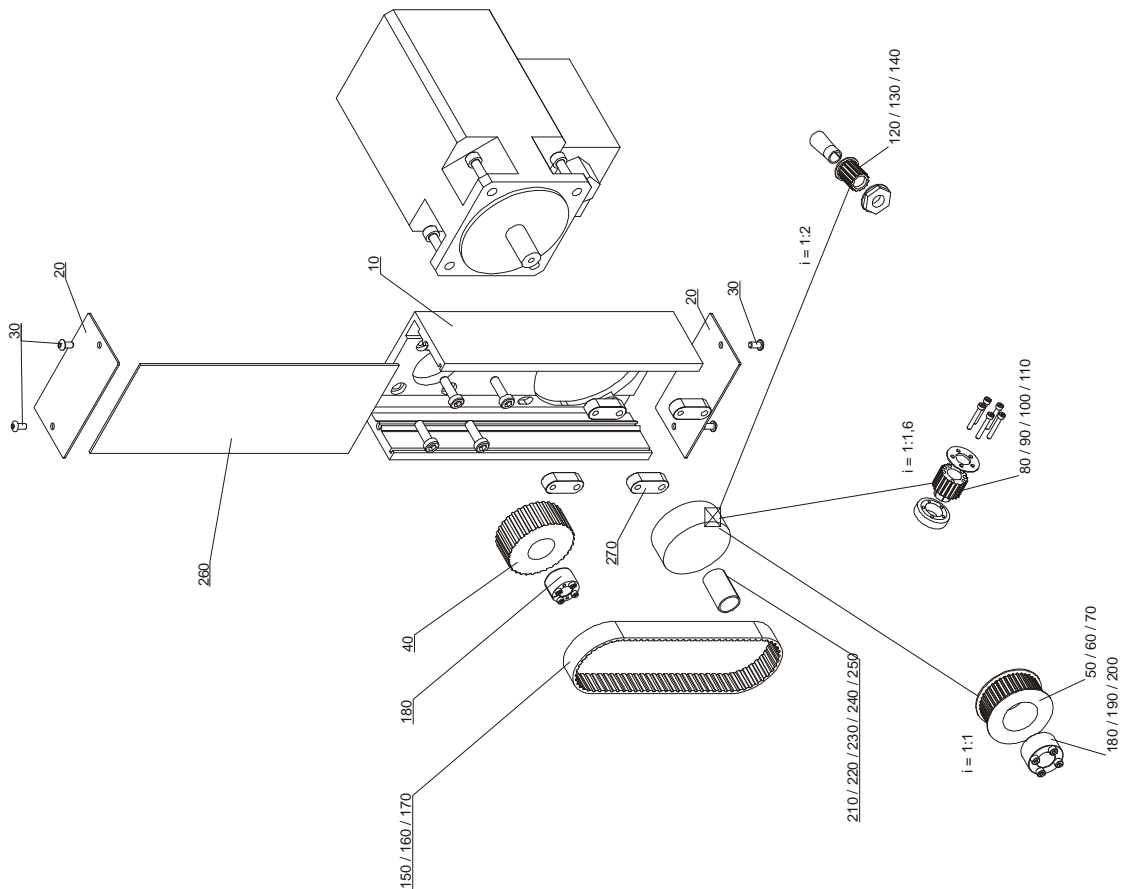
Explosion Riemengetriebe (TG 1000645)
